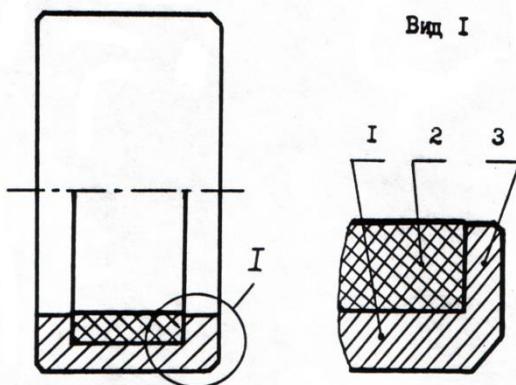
Общий вид втулки шарнирного подшипника технологического оборудования после изготовления: 1 – основа втулки; 2 – УУКМ; 3 – бурт
